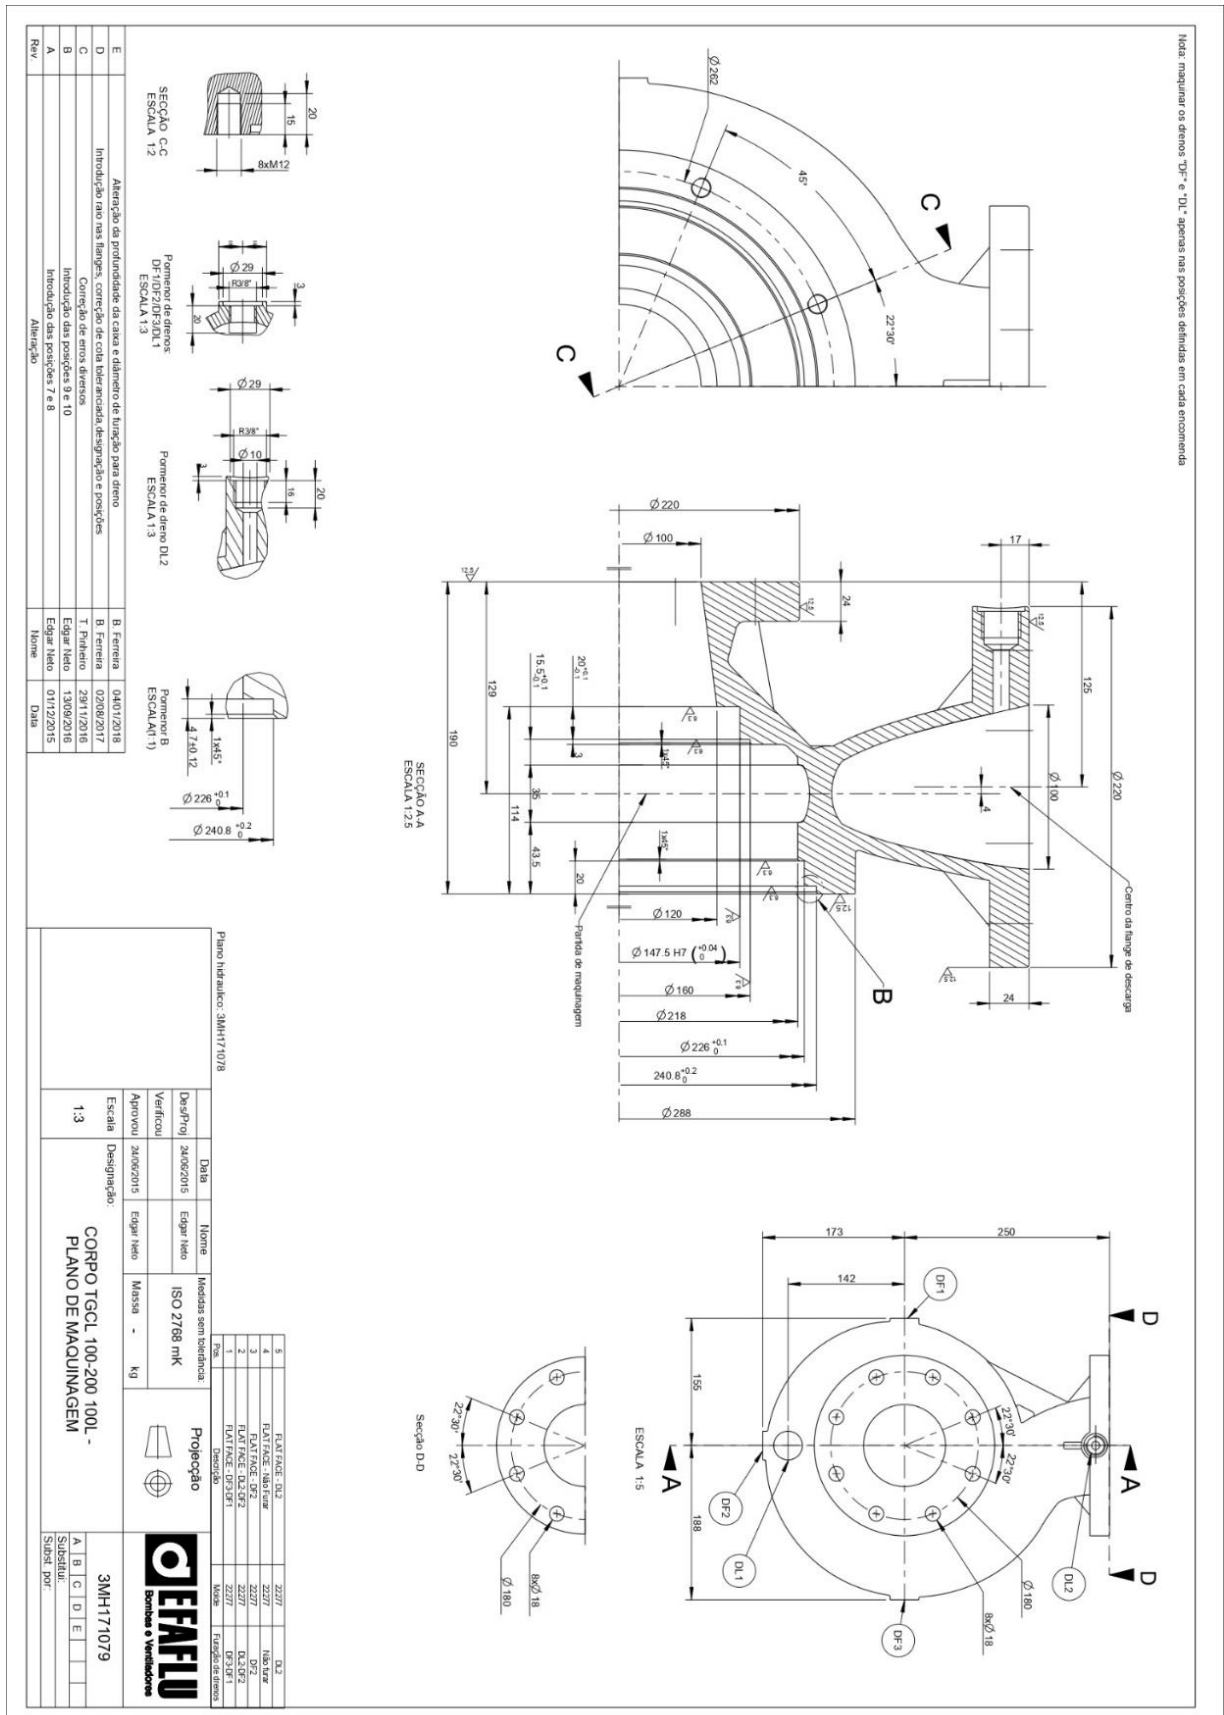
Desenho técnico do corpo da bomba TGCL100L.
